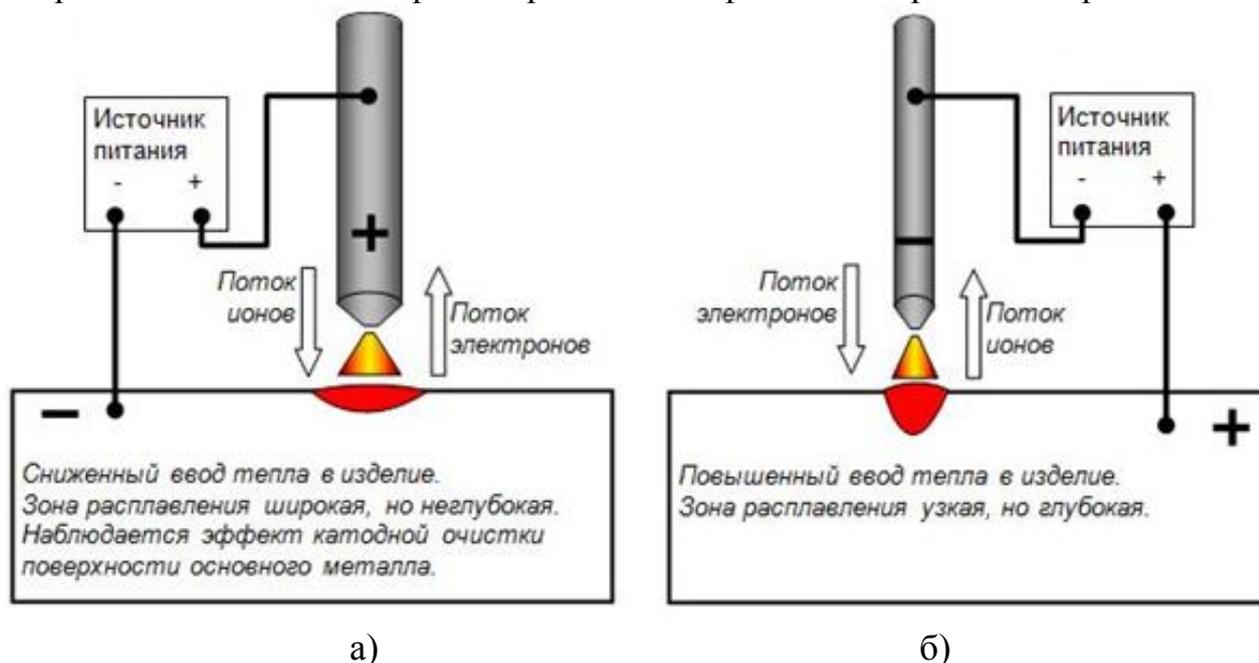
Схема подключения токовой цепи при работе со сварочным полуавтоматом:
